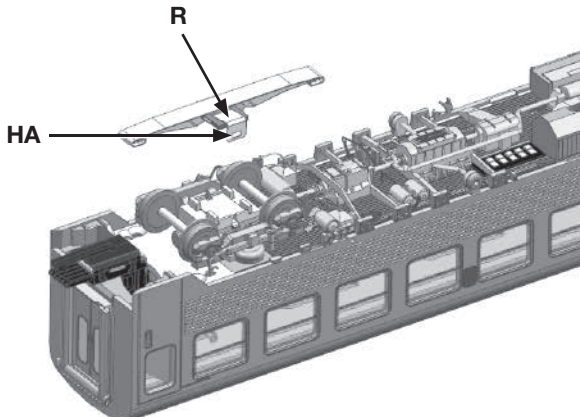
zeigt den ausgebauten Schleifer mit dem Haltebügel (R). Beim Einbau schnappt der Haltebügel einfach in zwei Haltenasen. Beim Demontieren drücken Sie bitte den Haltearm (HA) leicht mit einem Schraubendreher nach außen.
